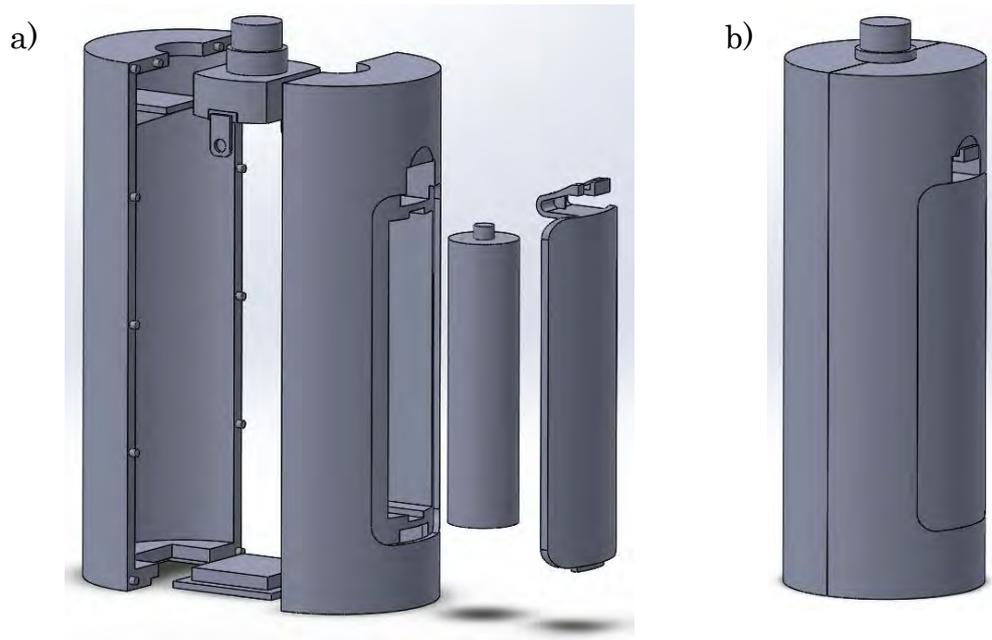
Linterna estilo orgánico, a) vista explosionada, b) vista de conjunto.
